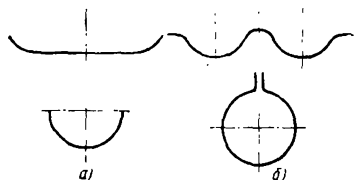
Способы гибки круглых деталей: а — полузакрытой; б — закрытой
